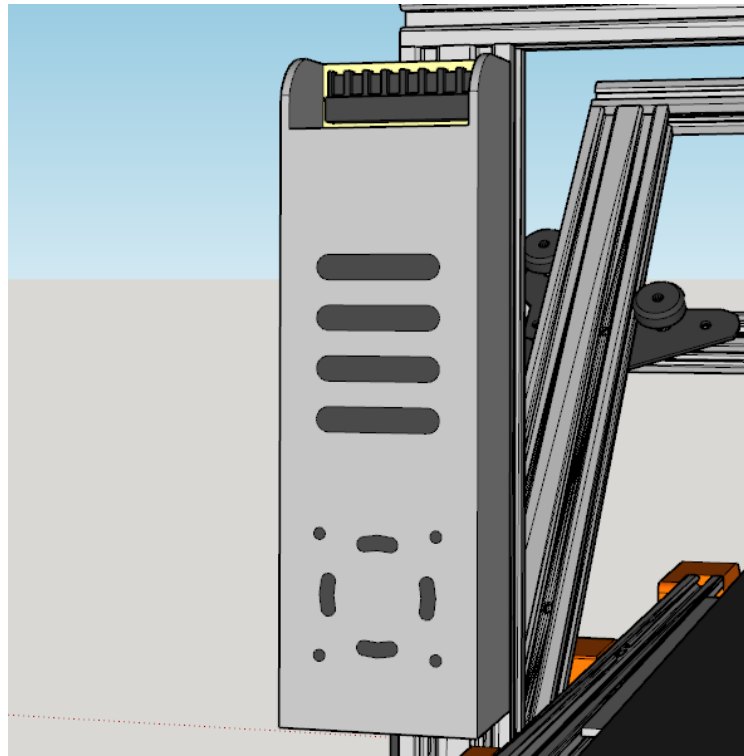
БЖ встановлений на корпусі принтера
